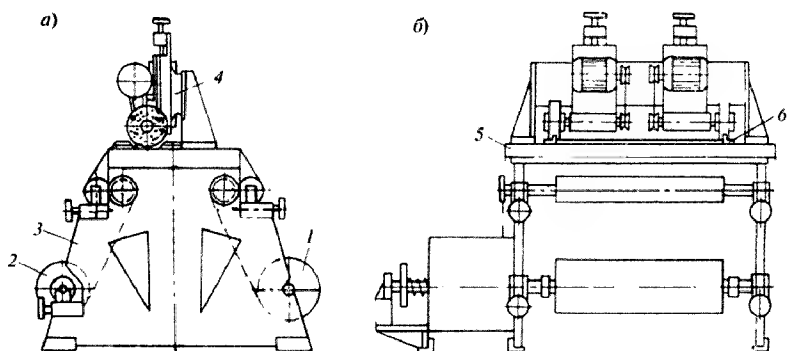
Общий вид станка модели 3Ш для зачистки кромок шлифшкурки:
